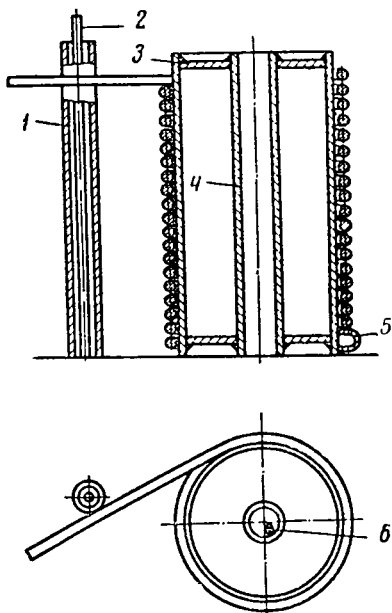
Схема приспособления для гибки цилиндрического змеевика
